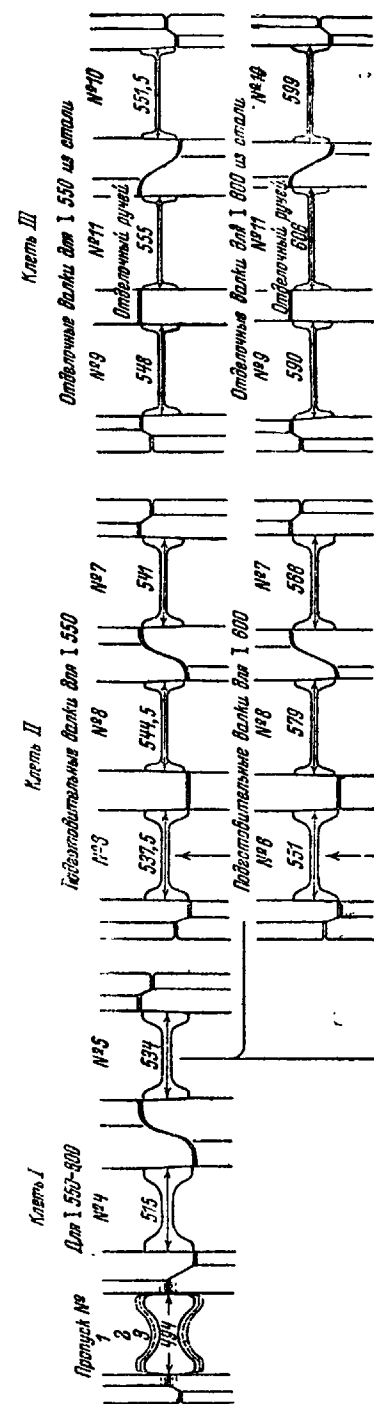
Калибровка балок № 60 и 55 на реверсивном стане дуо
